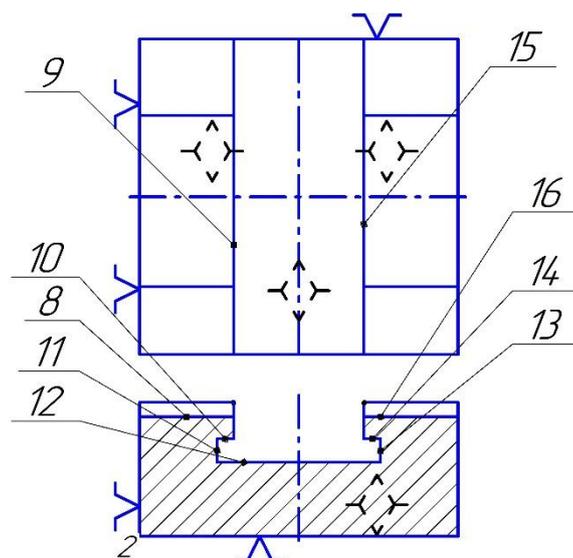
Поверхности для фрезерования с ЧПУ
